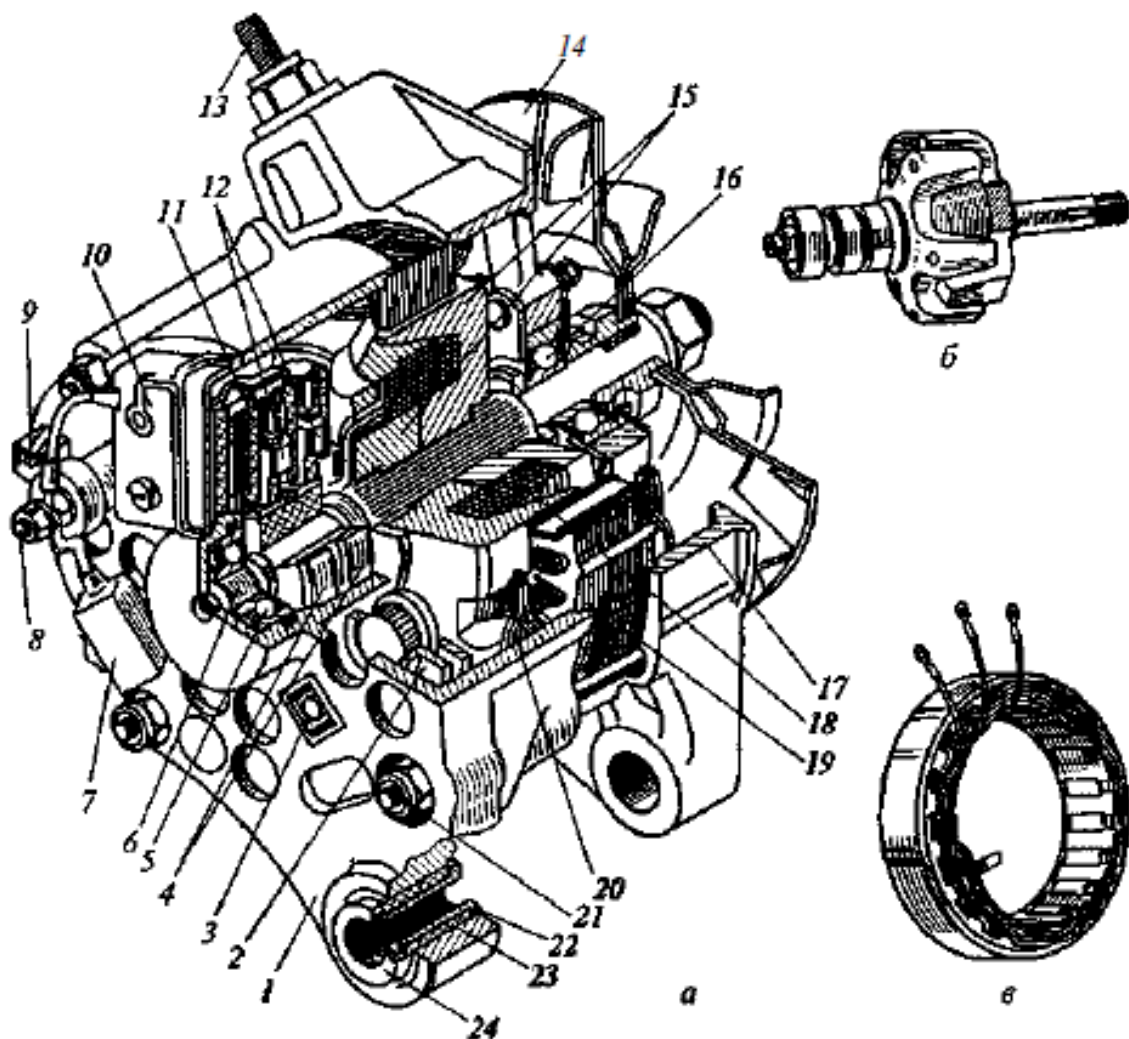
Генератор Г-222: а – общий вид; б – полюсные наконечники ротора; в – статор с обмоткой; 1 – крышка; 2 – блок выпрямителей; 3 – винт; 4 – контактные кольца; 5 и 16 – подшипники; 6 – вал; 7 – чехол вывода; 8 – вывод выходного напряжения; 9 – вывод обмотки возбуждения; 10 – крышка; 11 – щеткодержатель; 12 – щетки; 13 – болт; 14 – шкив; 15 – полюсные наконечники; 17 – корпус; 18 – обмотка ротора; 19 – сердечник статора; 20 – обмотка статора; 21 – стяжной болт; 22 – стальная втулка; 23 – резиновая втулка; 24 – шайба
